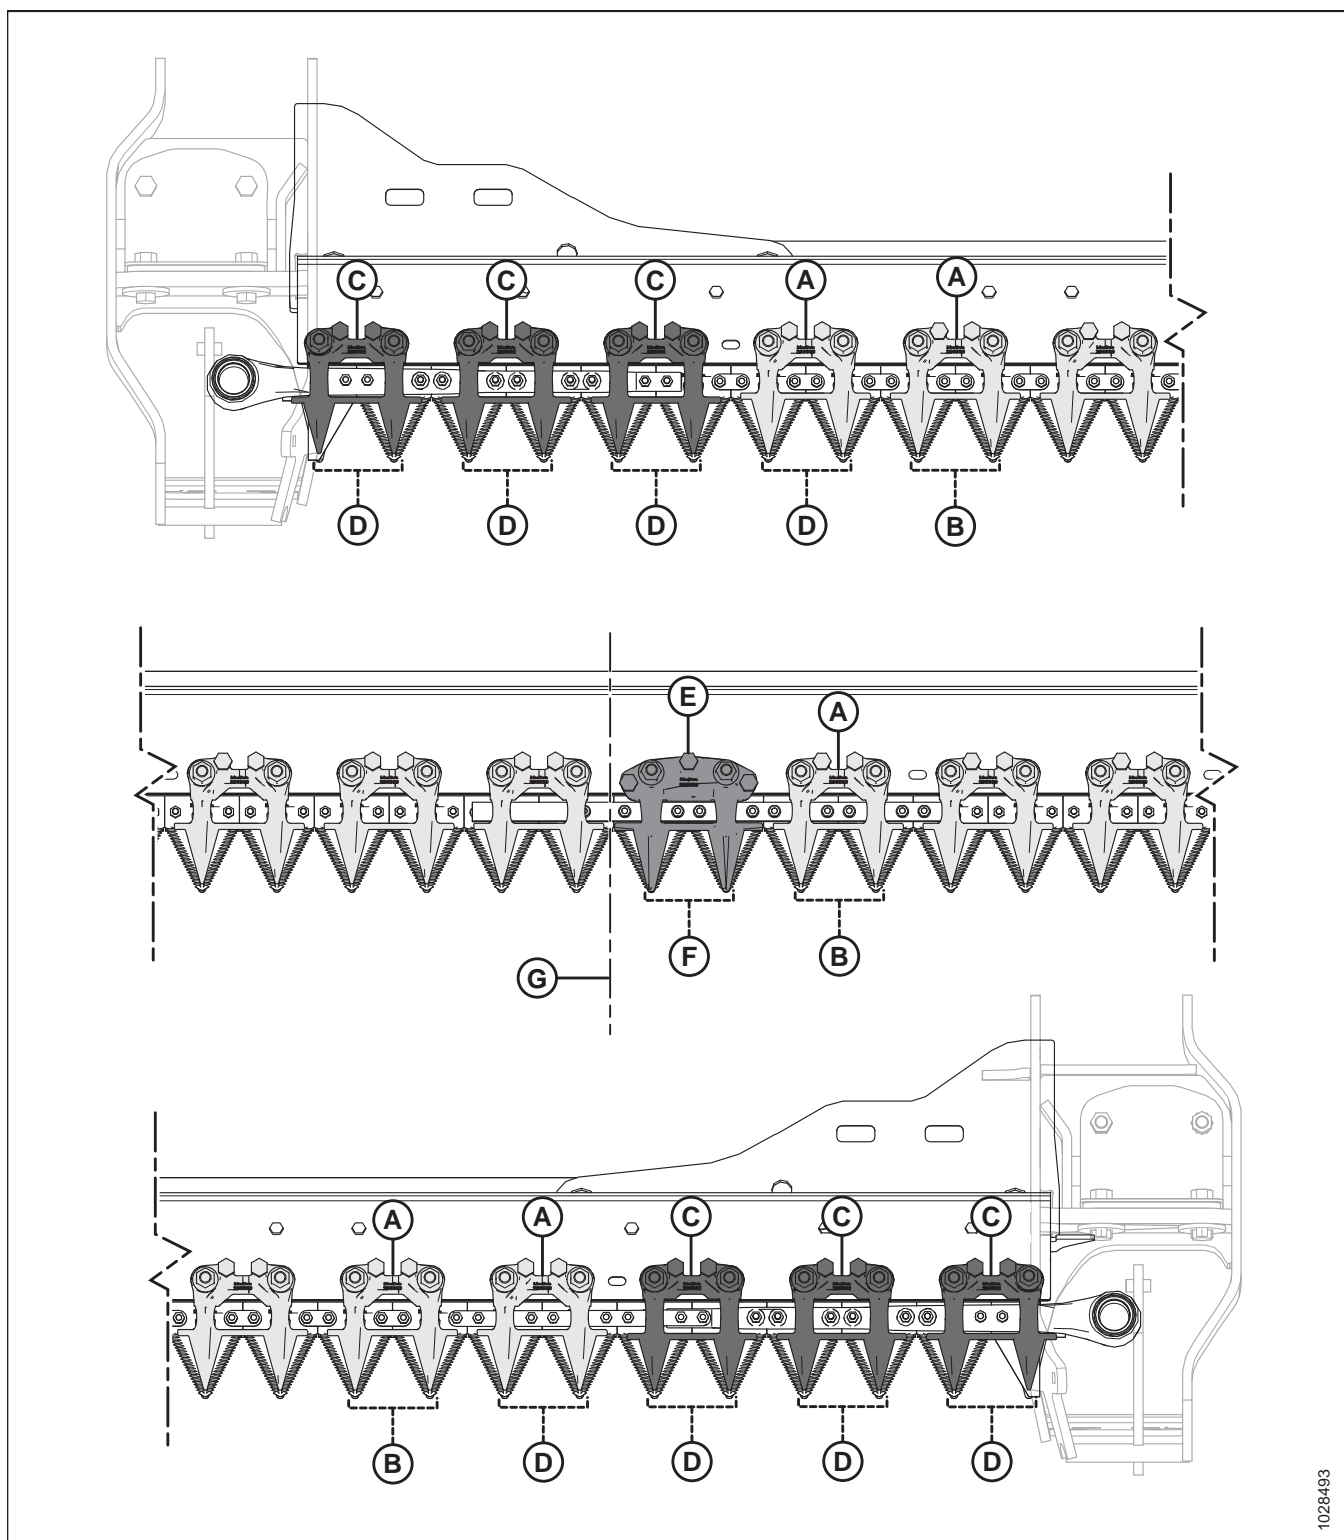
Местоположение коротких противорежущих пальцев и прижимов — жатка с двойным ножом FD241
